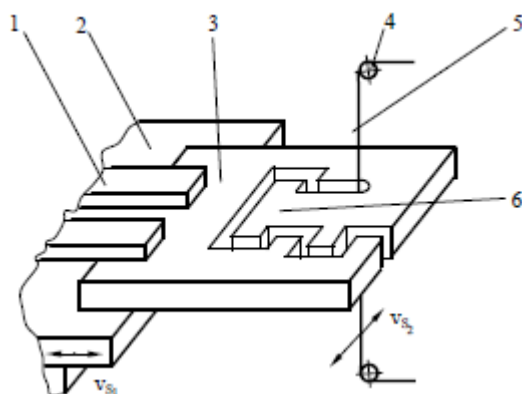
Кинематическая схема ЭЭО проволочным ЭИ: 1 – прихват; 2 – стол электроэрозионного станка; 3 – заготовка (матрица); 4 – направляющий ролик проволочного ЭИ; 5 – проволочный ЭИ; 6 – заготовка (пуансон); v_{s1} – движение подачи стола; v_{s2} – движение подачи проволочного ЭИ; ванна с диэлектрической рабочей жидкостью условно не показана
